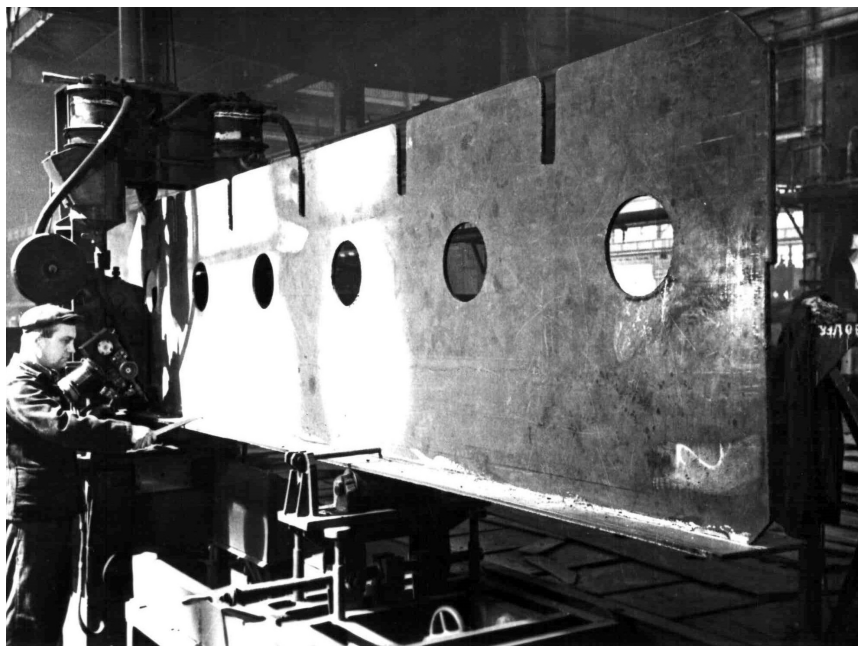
Зварювання симетричного тавра на верстаті СТС-2М
